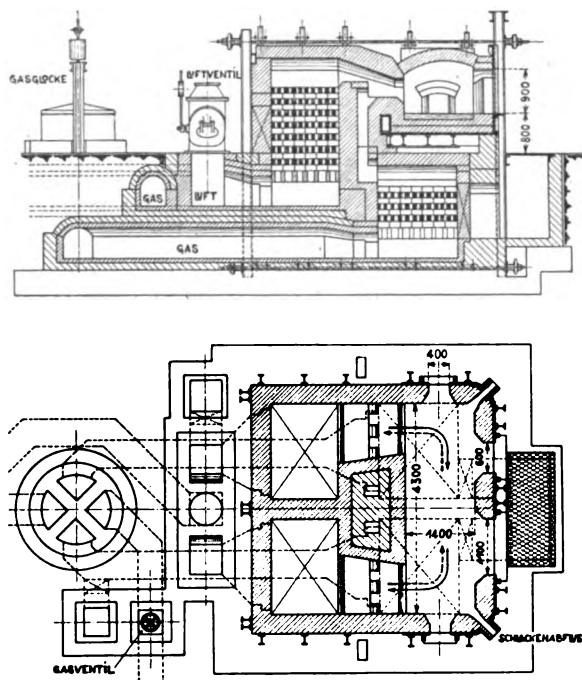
Schmiedeofen zum Wärmen von Maschinenteilen, mit Gasfeuerung und Regenerator. — Massstab 1:150.
